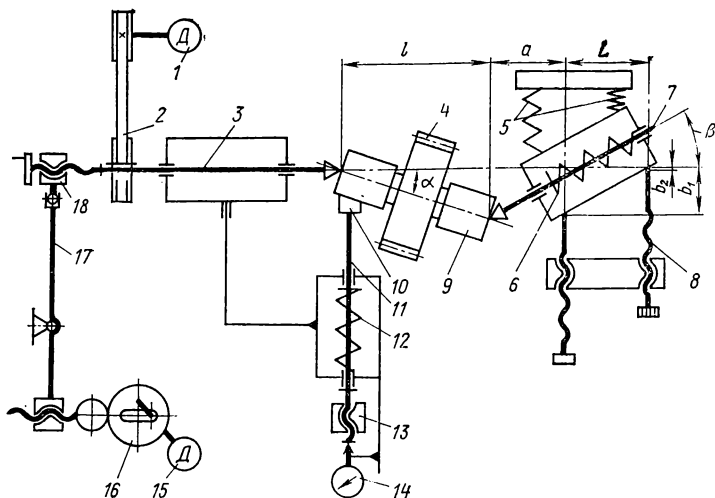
Кинематическая схема станка для доводки цапф шестерен:
